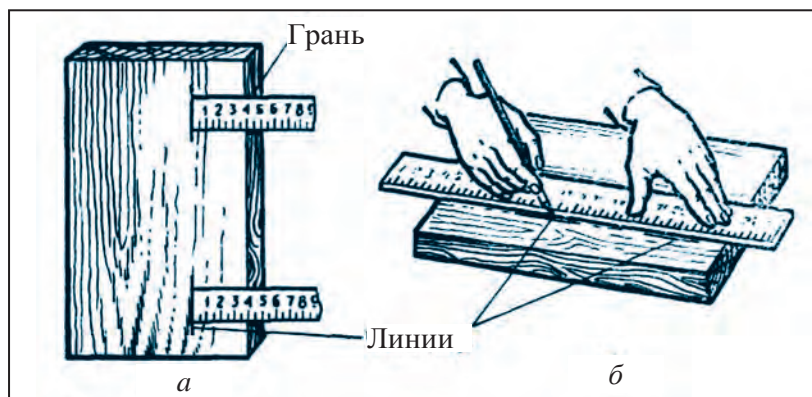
Разметка детали при помощи масштабной линейки: а) измерение ширины детали; б) проведение линии разметки.
